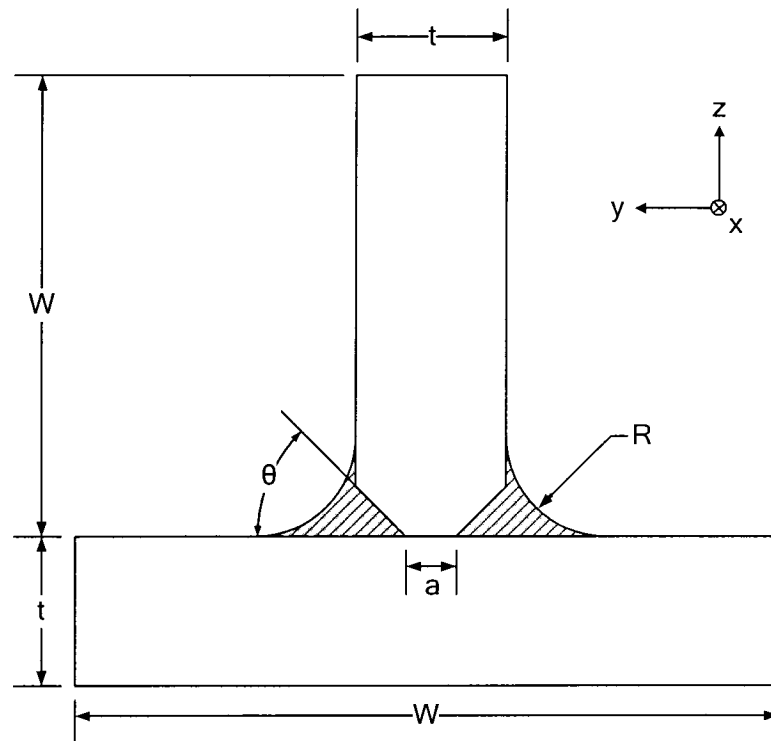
Géométrie des échantillons assemblés à l'aide des soudures
